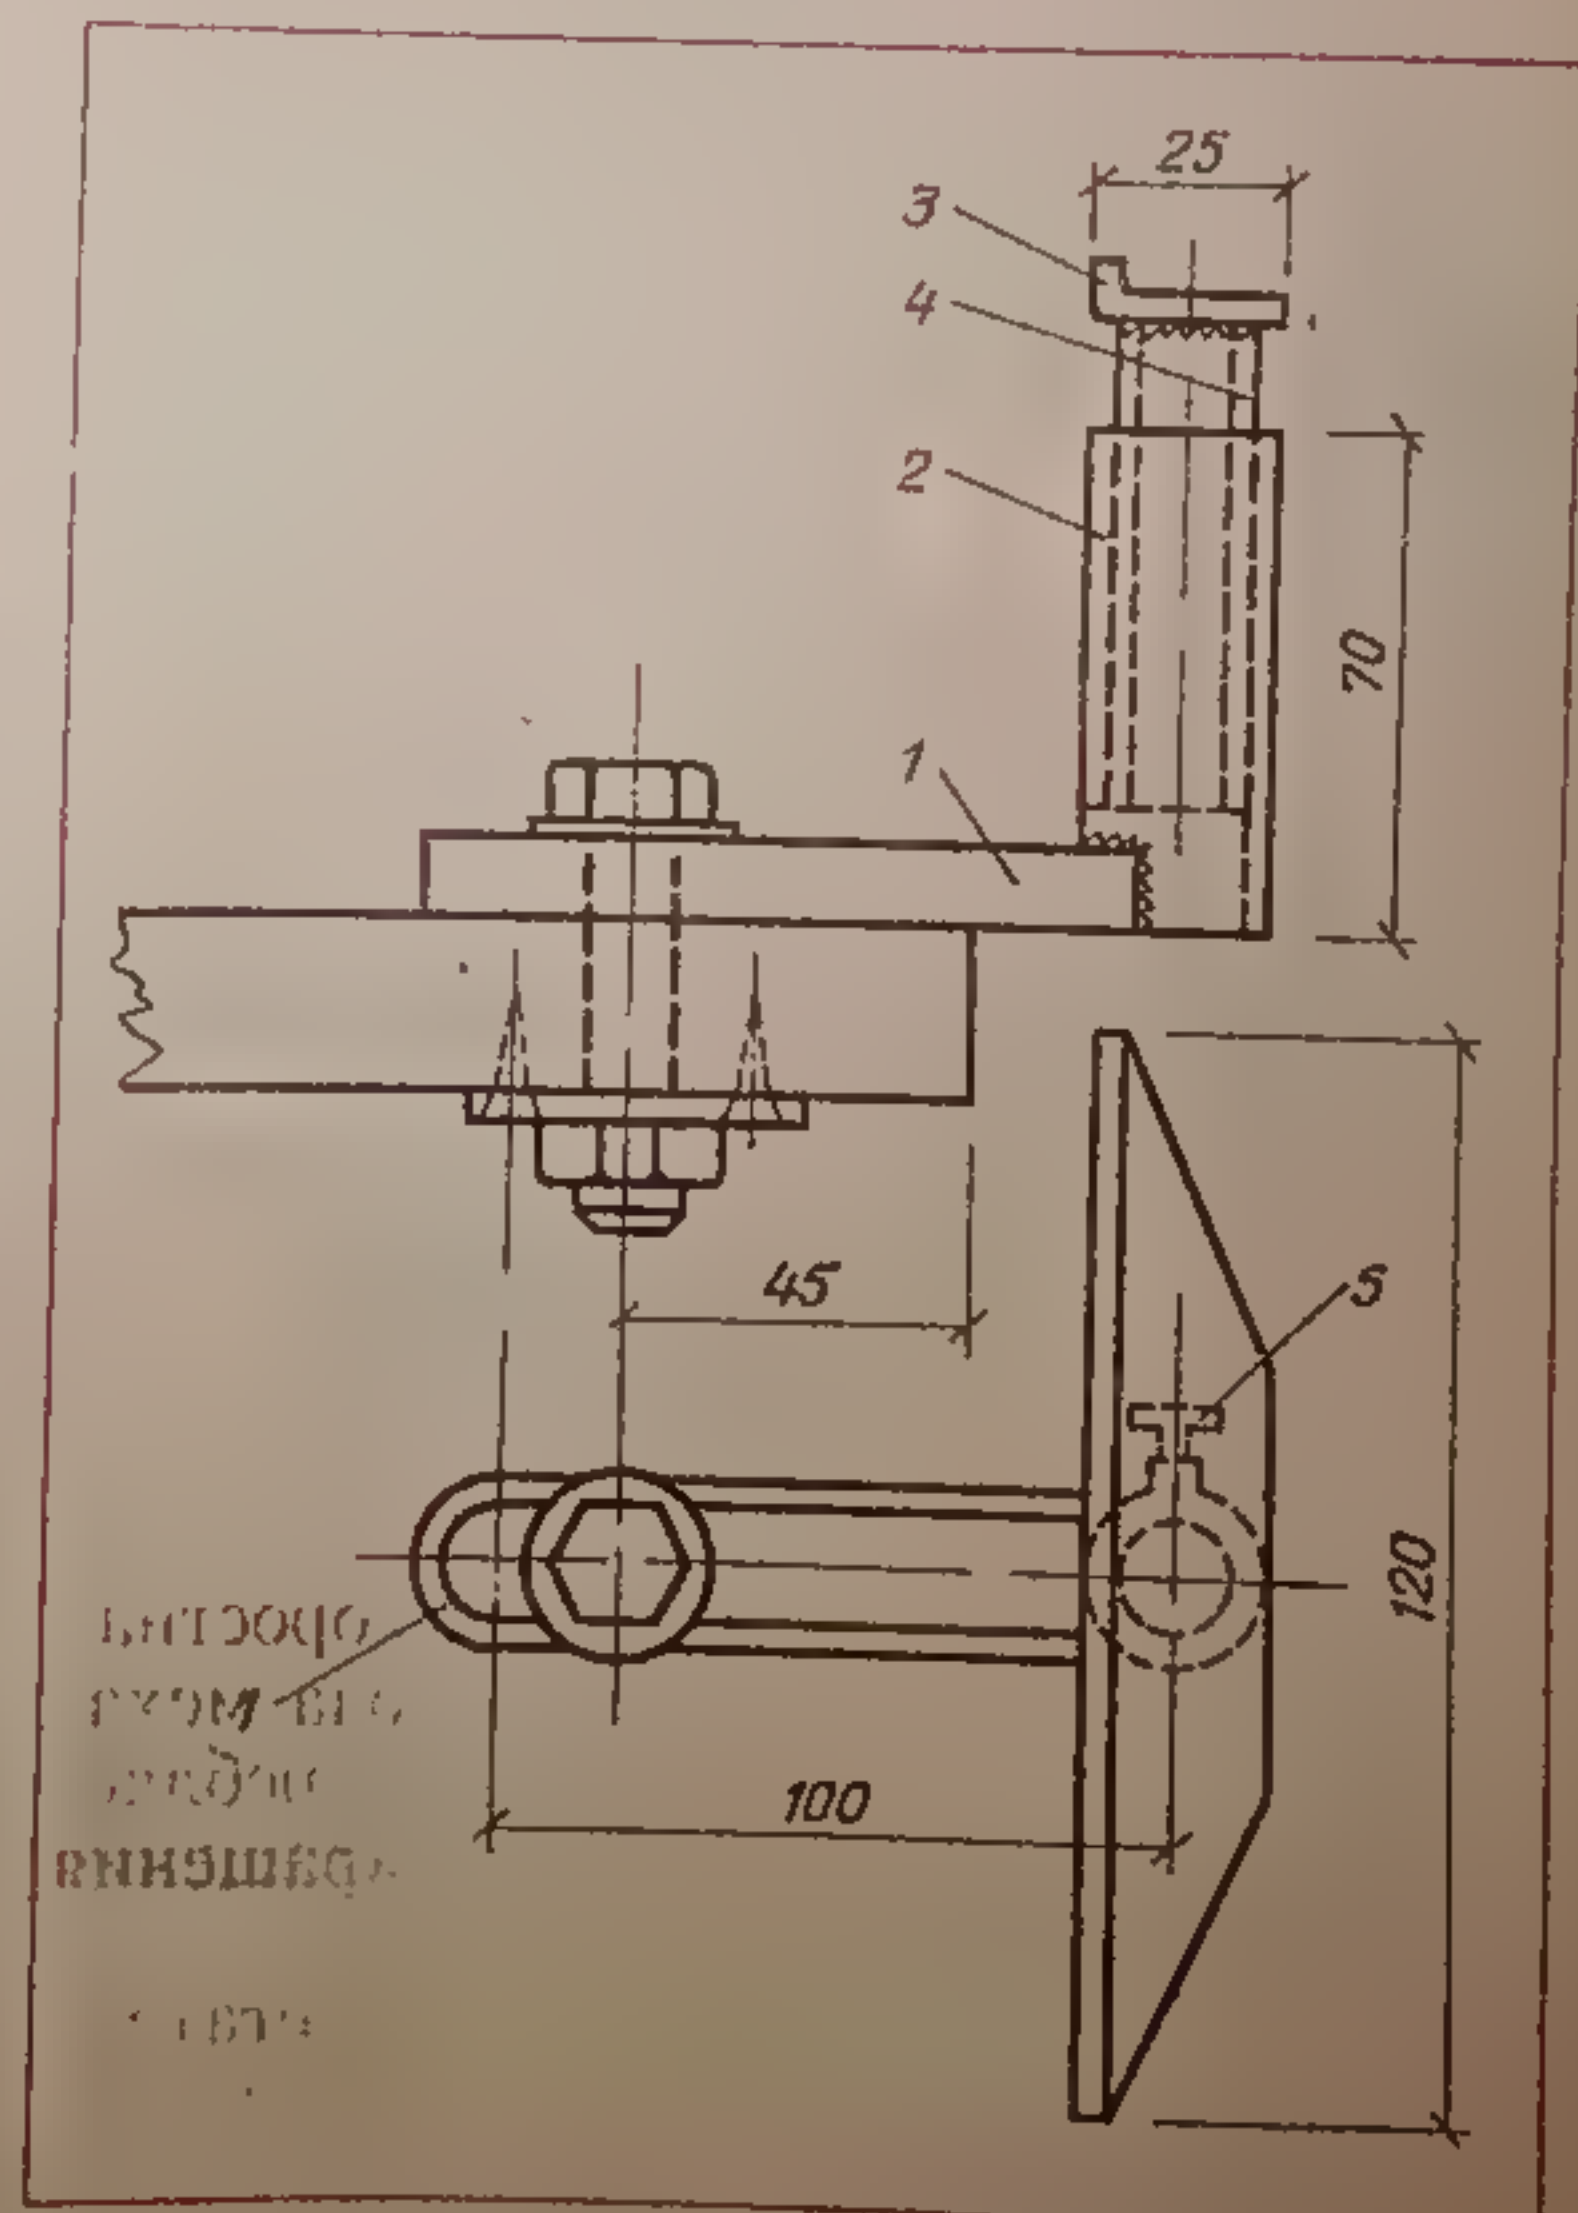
Приспособление для упора резца: 1 — скоба; 2 — трубка диаметром 28 мм (толщина стенки 2 мм); 3 — упор (уголок 25x10 мм); 4 — пруток диаметром 20 мм; 5 — стопорный винт
